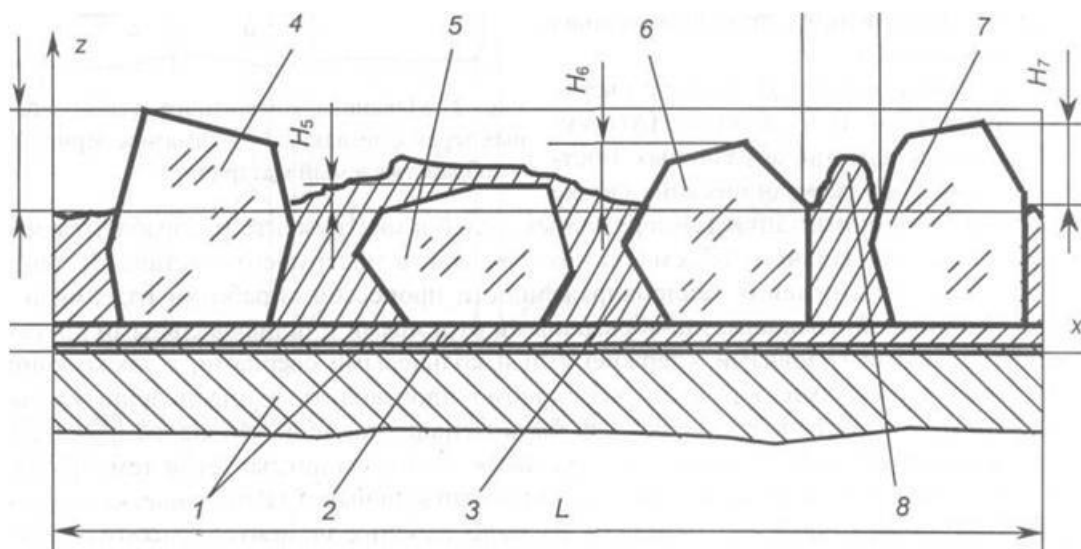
схема одношарового робочого шару алмазного інструмента:
